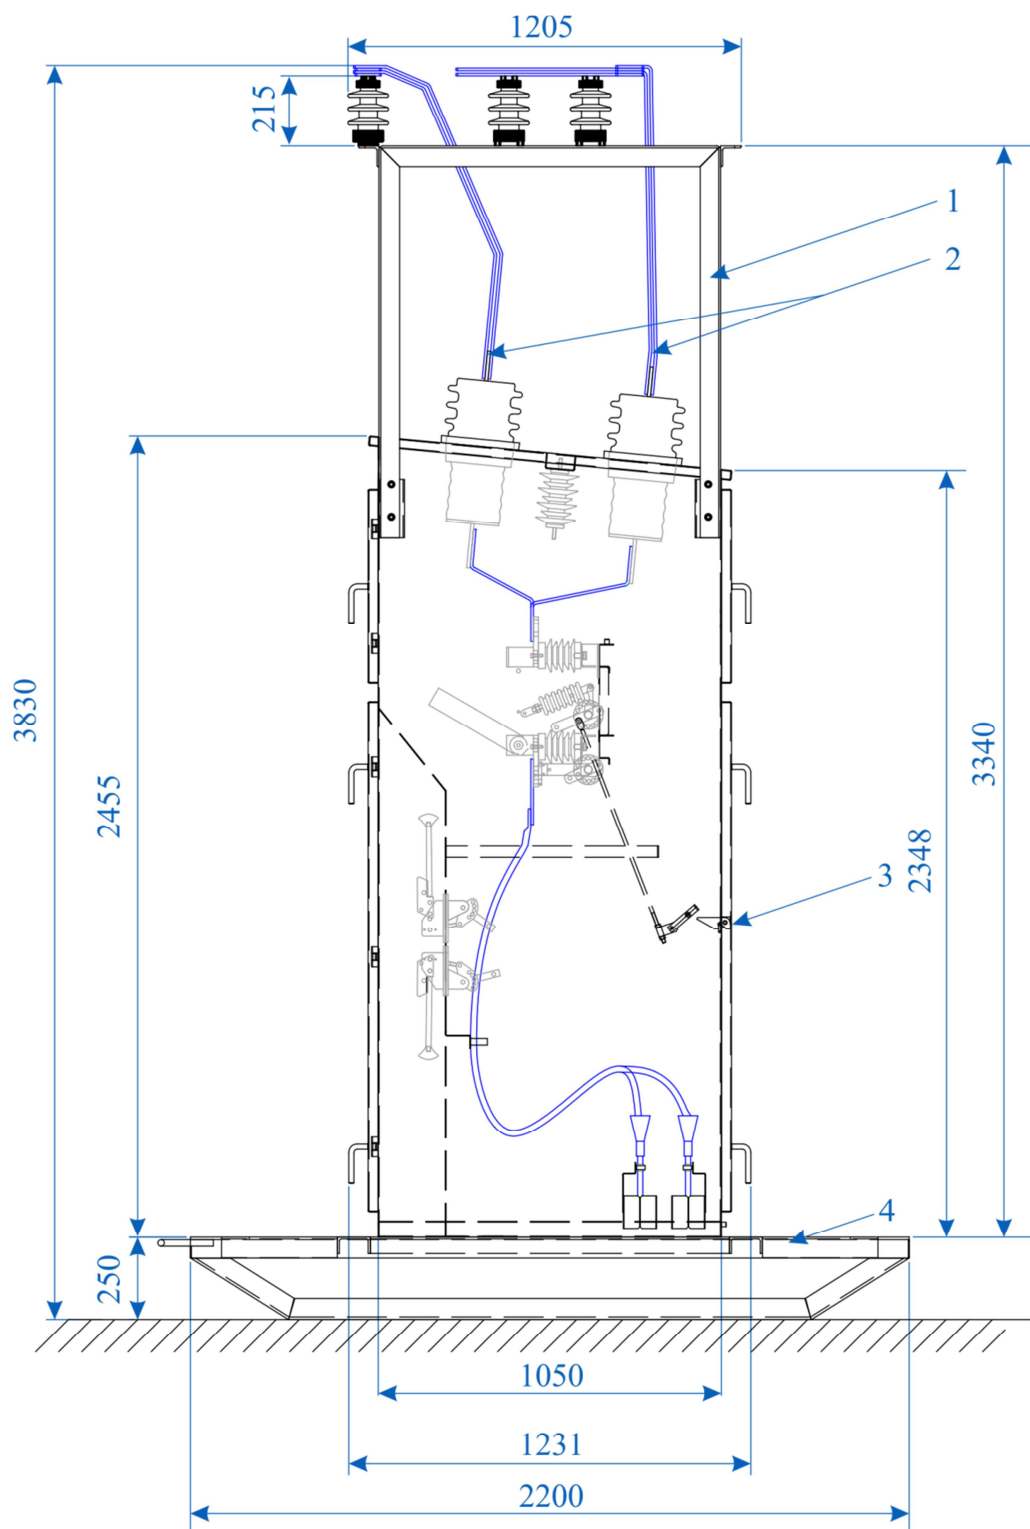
Габаритные размеры и устройство КРН с вакуумным выключателем
